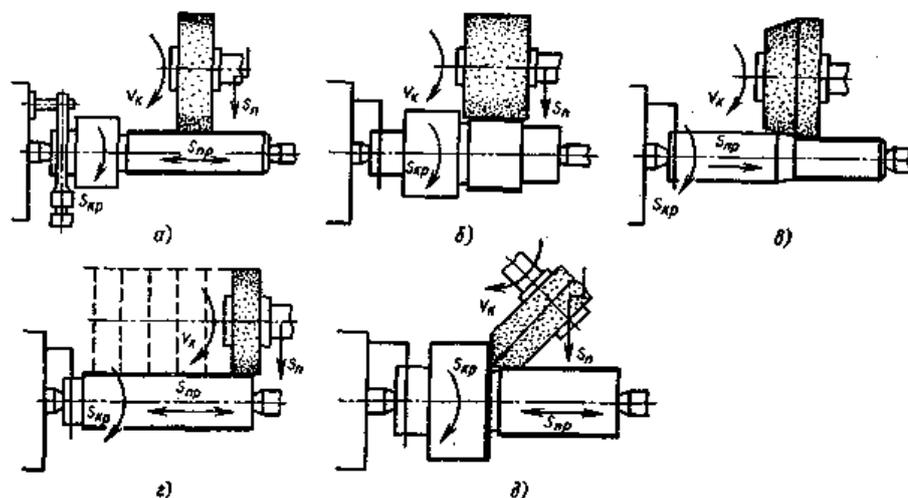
Схемы обработки заготовок на круглошлифовальных станках
